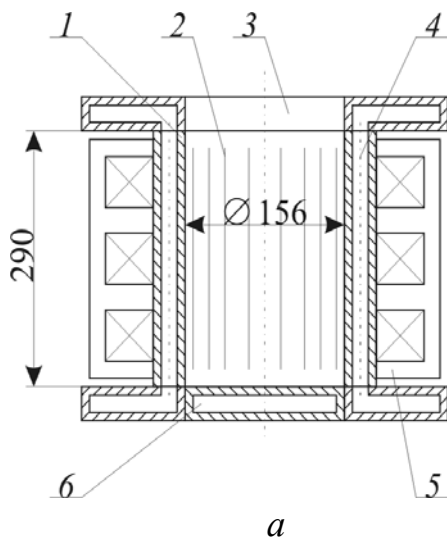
Схема (а) і загальний вигляд (б) кристалізатора для одержання трубної заготовки:
